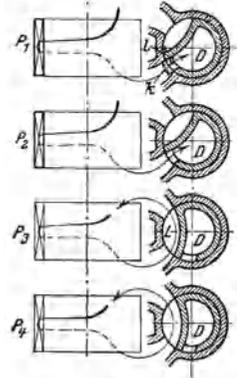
Steuerschema des Lenz-Getriebes. (Dieselmaschinen II. S. 70.)
